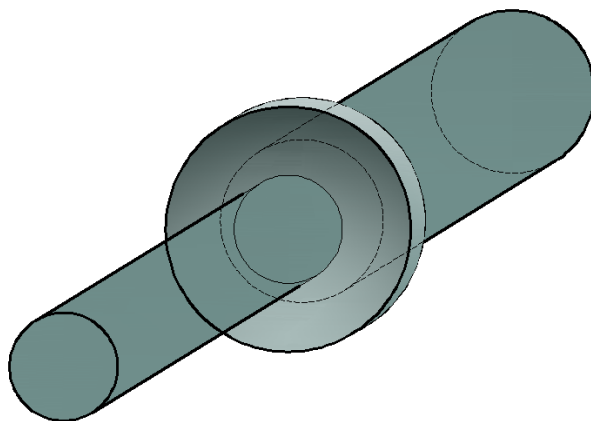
Основная деталь предлагаемой конструкции лебёдки.
